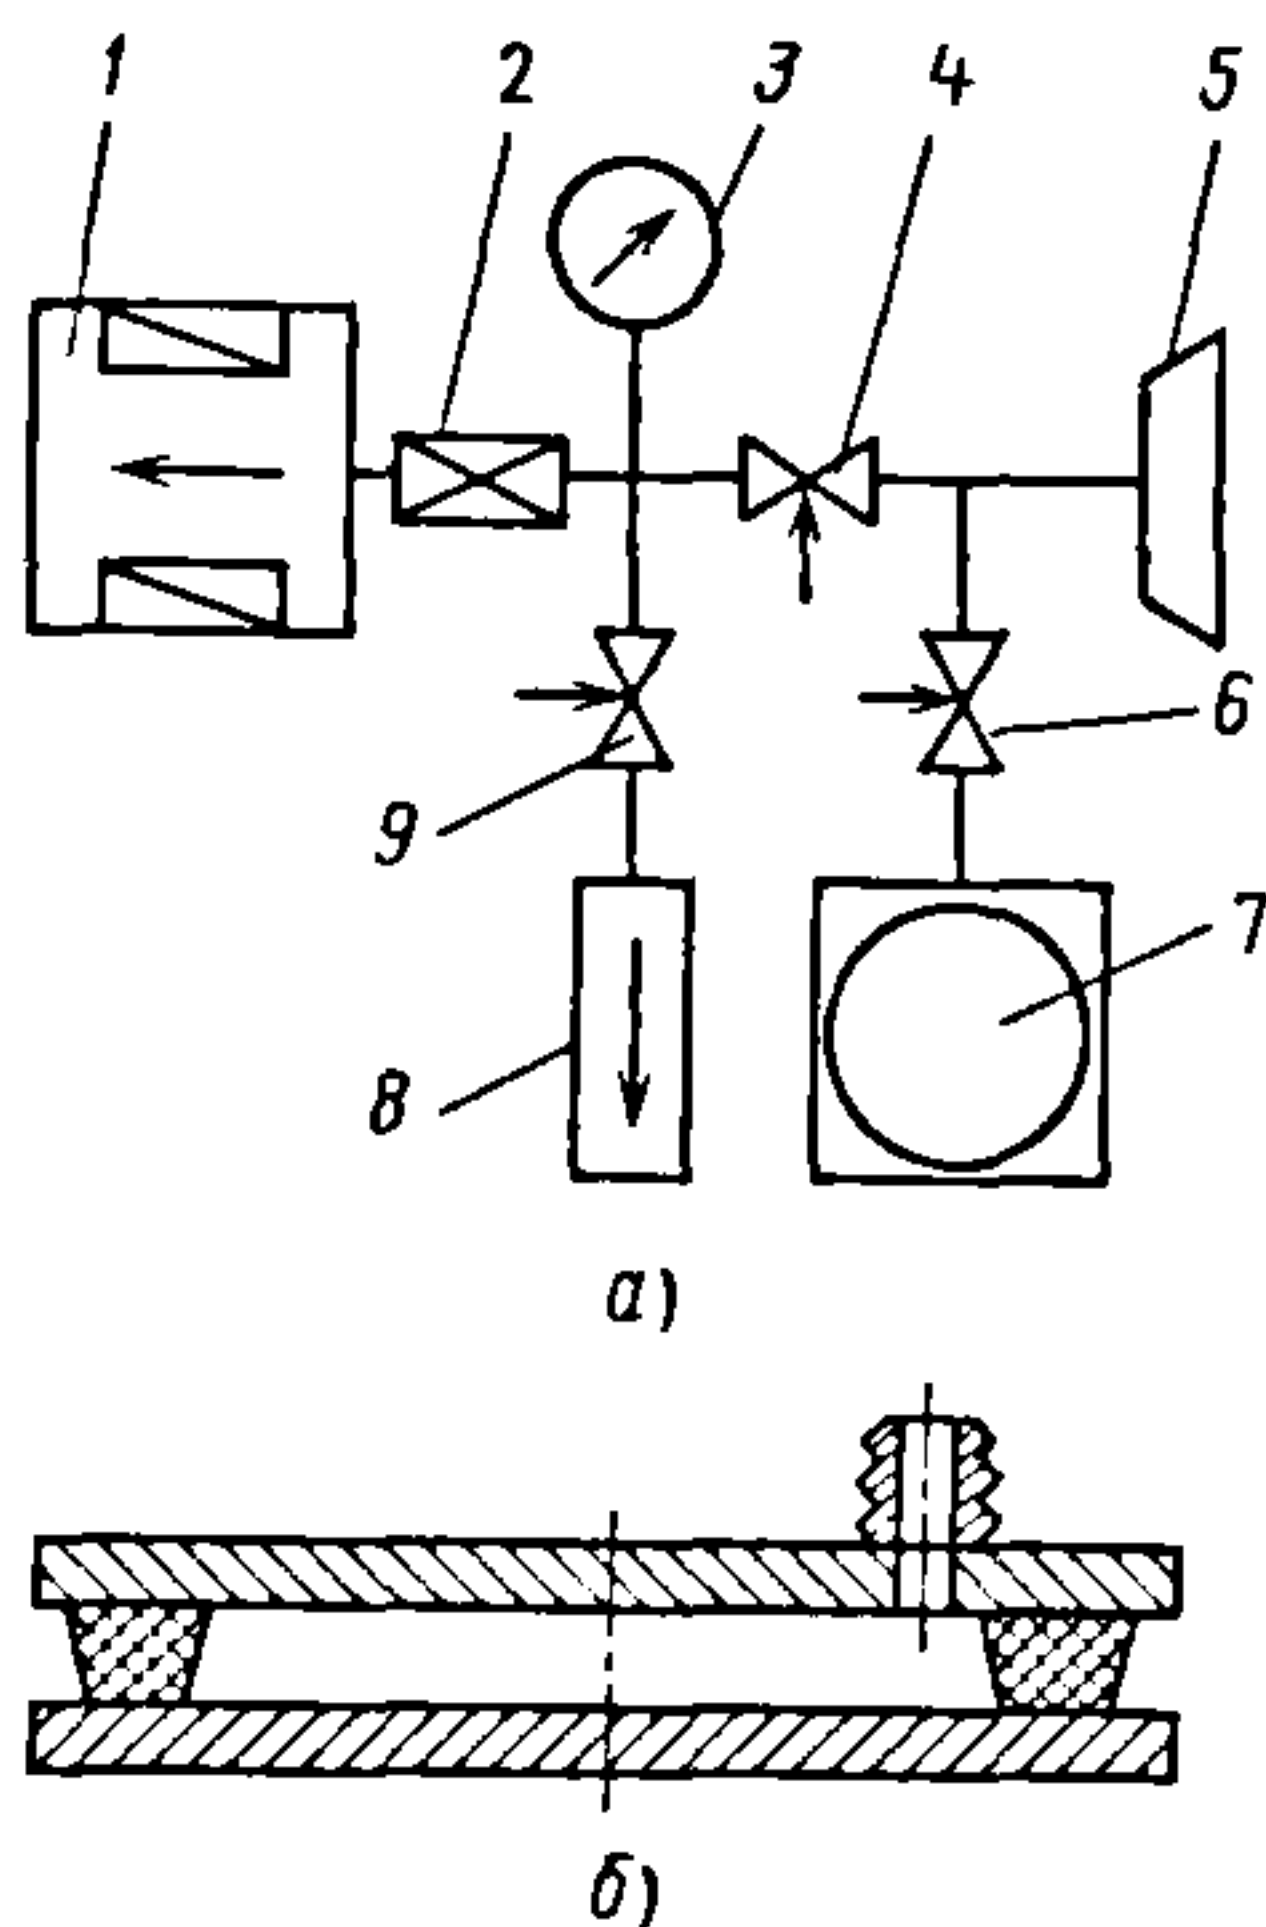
Схема испытаний на герметичность с помощью вакуумных присосок: а — схема установки (1 — теченскатель; 2 — дроссельный клапан теченскателя; 3 — манометрический преобразователь; 4, 6, 9 — клапаны; 5 — вакуумная присоска; 7 — механический вакуумный насос; 8 — течь «Гелит»); б — присоска
